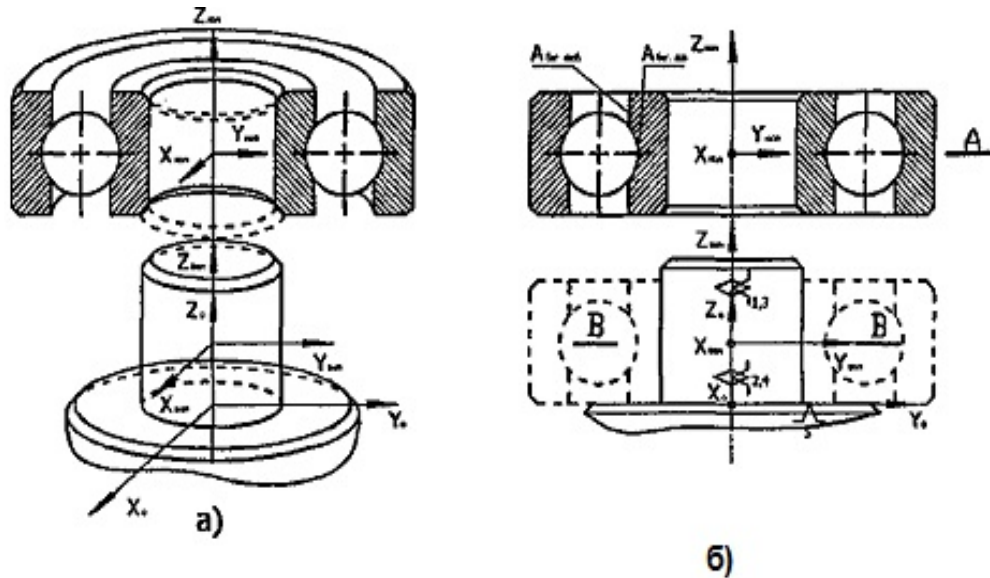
Расположение подшипника относительно шейки вала до его запрессовки
